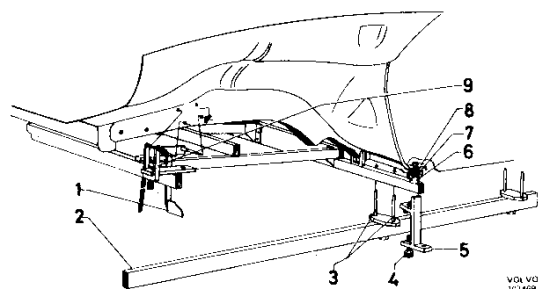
Werkzeuge zur Vermessung des vorderen Längsträgers 164
